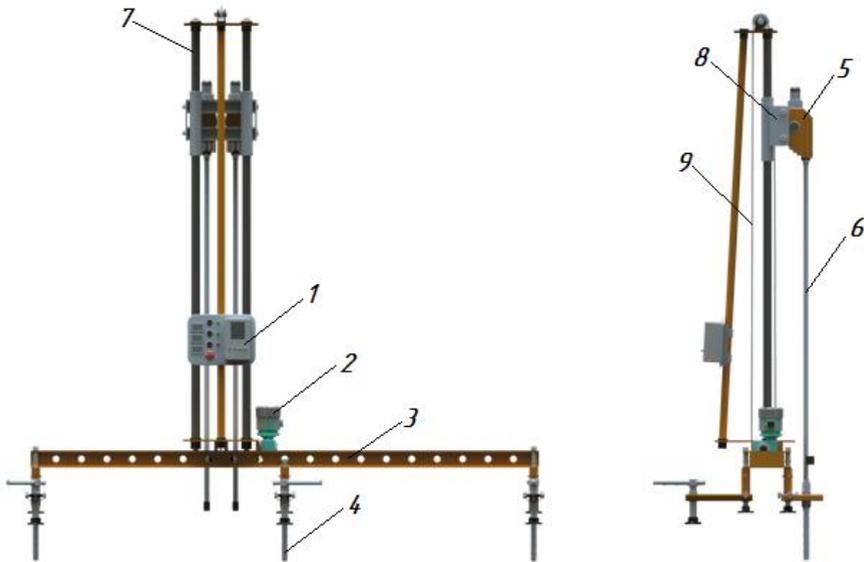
Общий вид бурового станка строчечного бурения БС-32: 1 – пульт управления; 2 – подающий механизм; 3 – рама станка; 4 – анкер; 5 – перфоратор; 6 – штанга; 7 – направляющая буровой каретки
